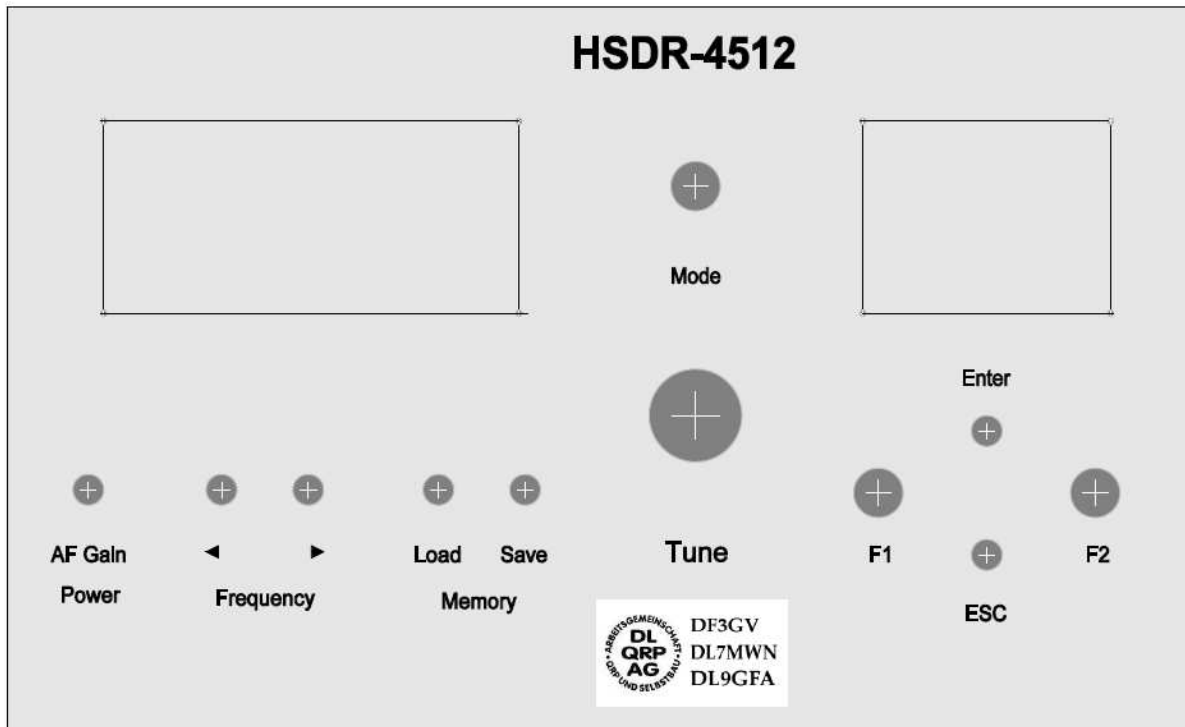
So sieht dann die endgültige Frontplatte im FrontDesigner aus
